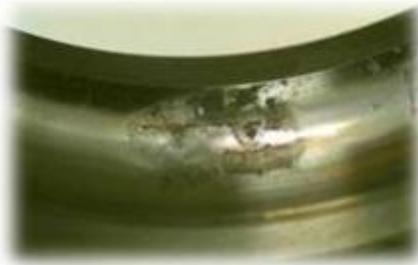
DEFAUT DE ROULEMENT – CORROSION. [59]
